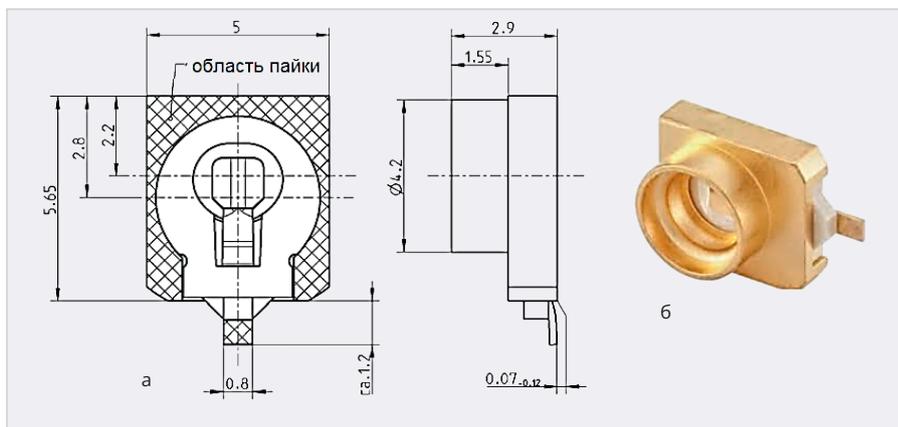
Конструкция (а) и внешний вид (б) соединителя FMC-розетка для поверхностного монтажа
